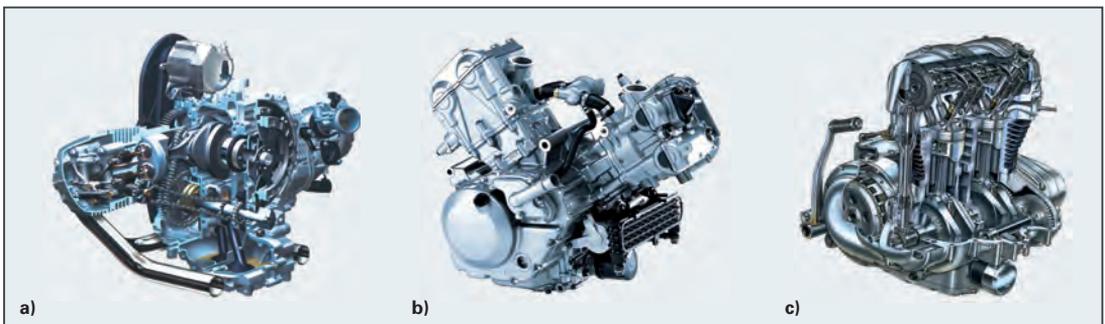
Anordnung der Zylinder a) Boxermotor b) V-Motor c) Reihenmotor
